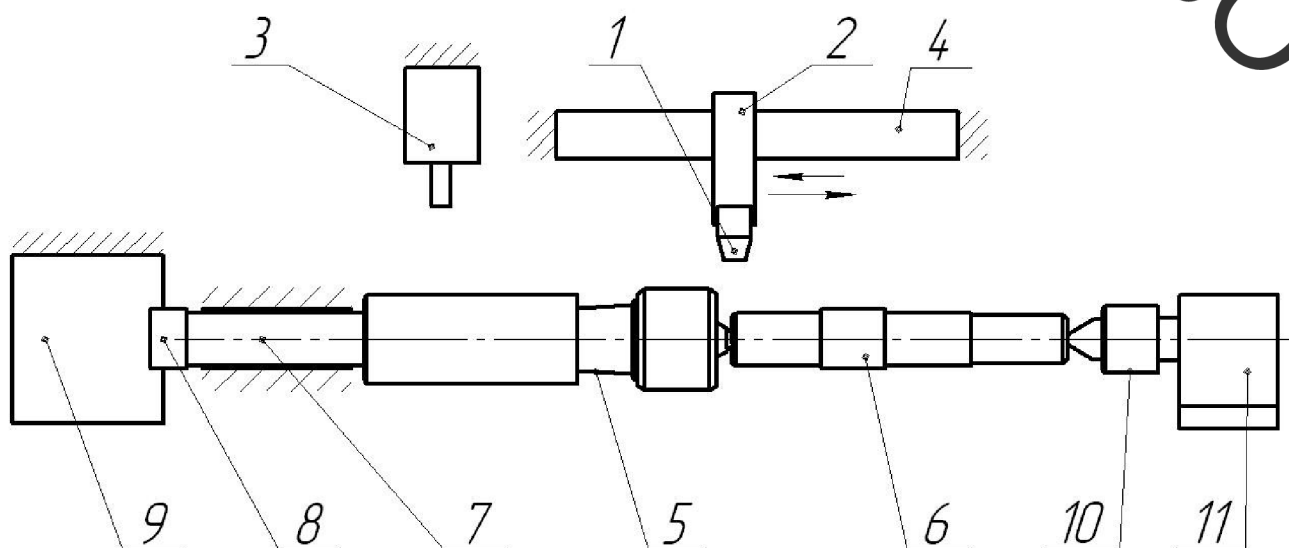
Конструктивна схема установки відновлення вала черв'ячного редуктора
